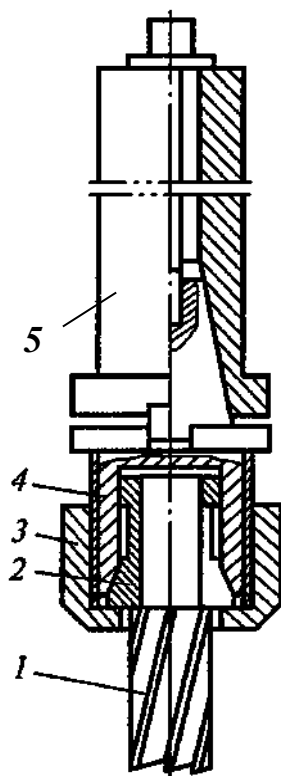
Установка концевой фрезы с цилиндрическим хвостовиком в патроне и шпинделе станка: 1- фреза; 2 – цанга; 3 – гайка;
